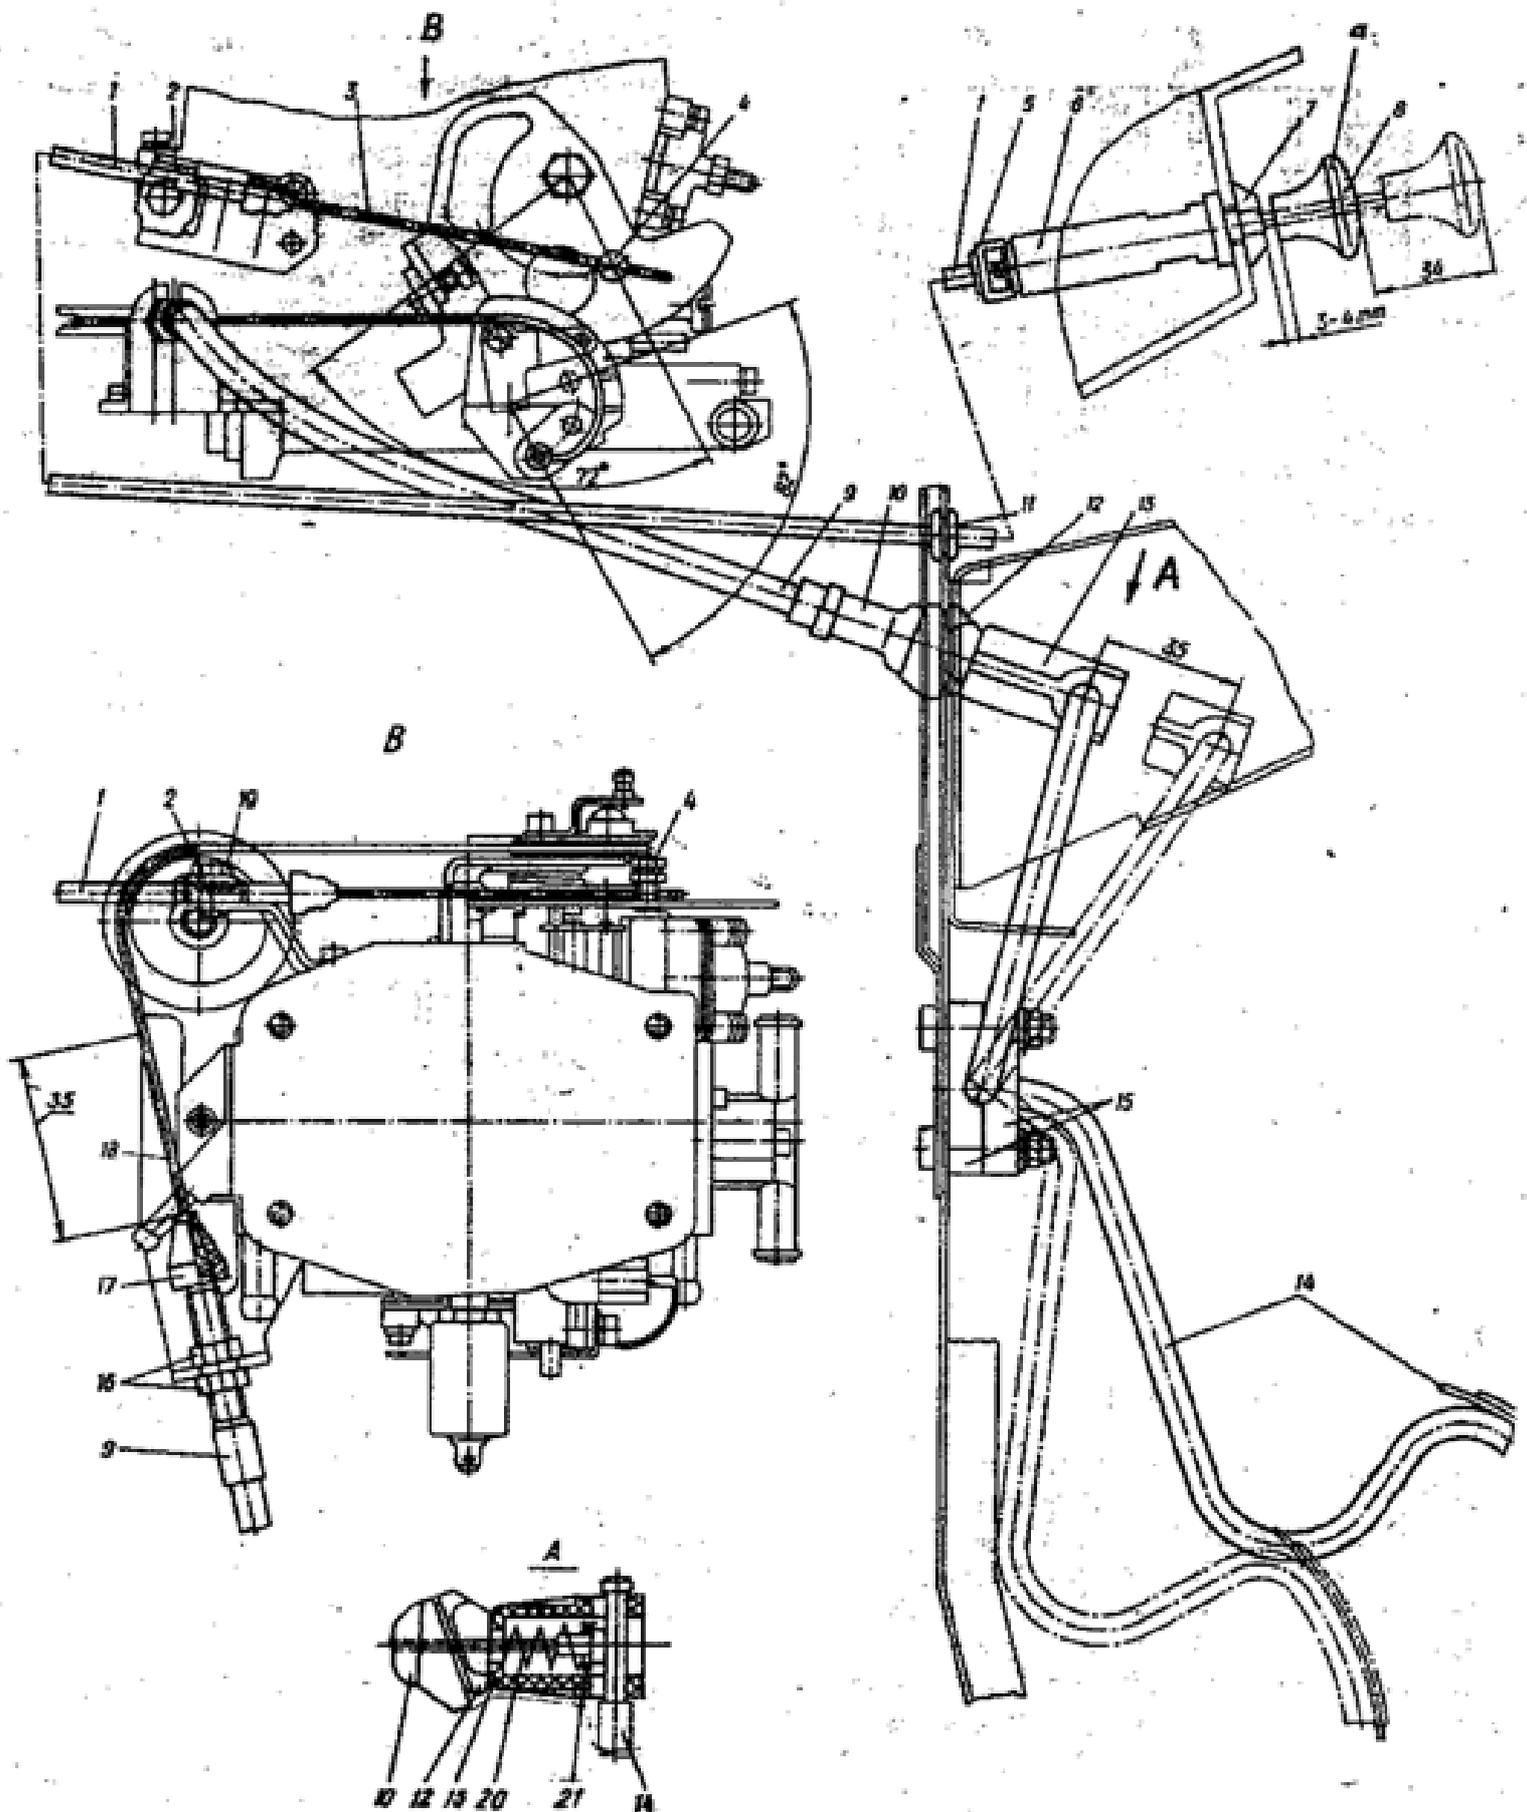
Подсоединение приводов карбюратора 21081-1107010: 1 - оболочка тяги привода воздушной заслонки; 2 - прижимная пластина; 3 - тяга привода воздушной заслонки; 4, 19 - болт; 5 - фиксатор; 6 - кронштейн; 7 - гайка кронштейна; 8 - ручка; 9 - оболочка тяги привода дроссельной заслонки; 10 - наконечник оболочки; 11 - втулка уплотнительная; 12 - упор педали; 13 - корпус; 14 - педаль акселератора; 15 - опора педали; 16 - гайка крепления тяги акселератора; 17 - уплотнитель; 18 - тяга акселератора; 20 - пружина компенсационная; 21 - фиксатор тяги
